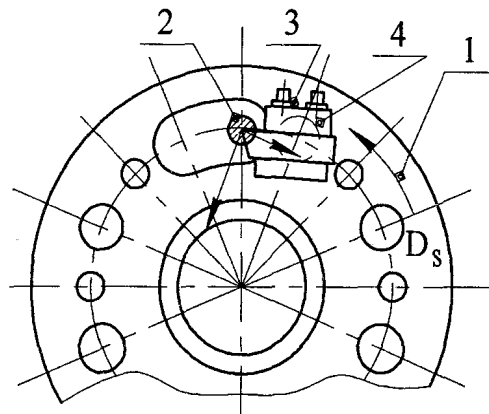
Установка радіального різця на револьверних верстатах з паралельними осями шпинделя і револьверної головки: 1 - револьверна головка; 2 - оброблювана заготовка; 3 - різець; 4 - державка для різця
